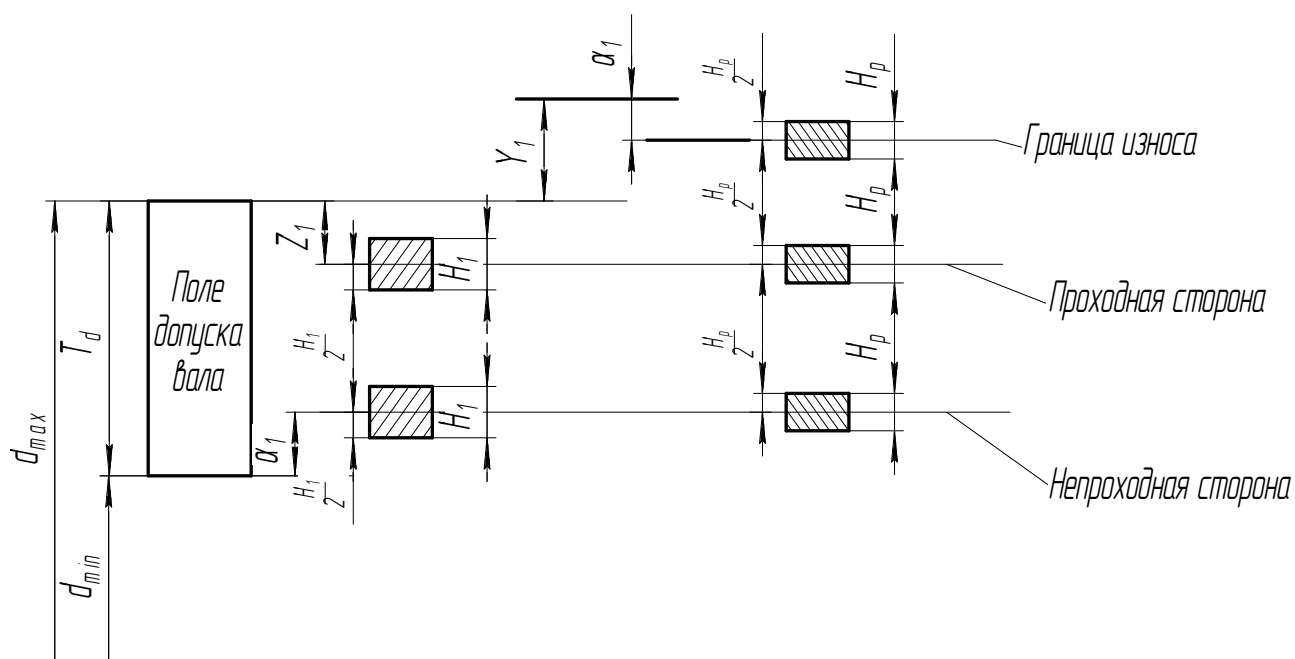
Схема расположения полей допусков калибров для контроля валов и контракалибров
